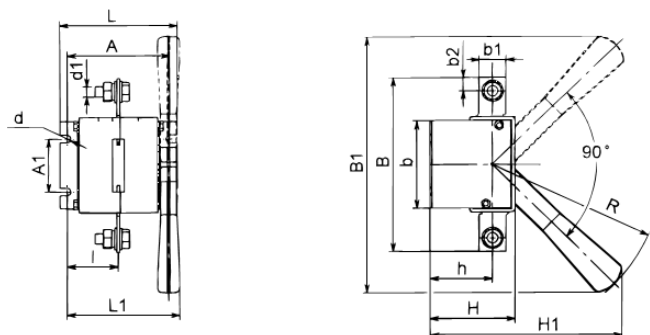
Б Выключатель-разъединитель на одно направление однополюсный с боковой рукояткой
